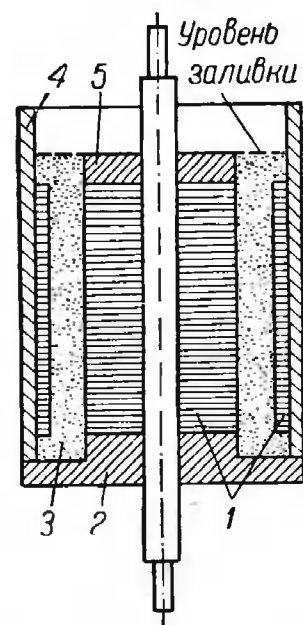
Форма для перезаливки алюминием короткозамкнутой обмотки ротора: 1 — тело ротора; 2 — нижнее ступенчатое кольцо; 3 — заливка; 4 — трубка-форма; 5 — верхнее кольцо.
